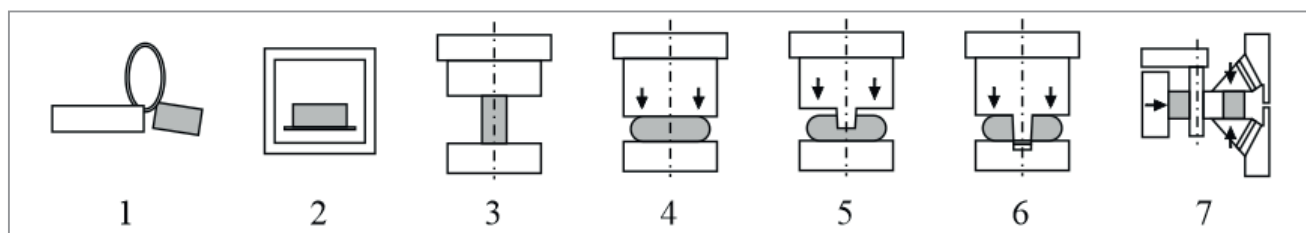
Технологический процесс изготовления кольцевых заготовок:
